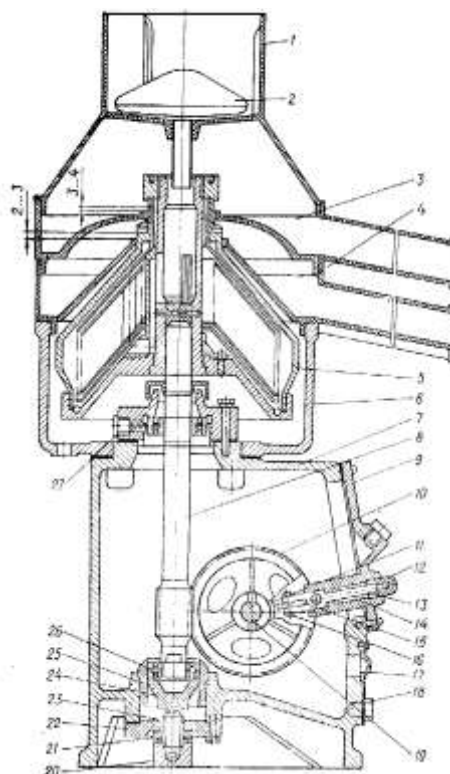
Сепаратор сливковідокремлювач ОСБ: 1 – поплавок камера; 2 – поплавок; 3 – прийомник для сливок; 4 – прийомник для обезжиреного молока; 5 – барабан; 6 – чаша станини; 7 – станина; 8 – вертикальний вал; 9 – кришка; 10 – черв’ячна шестерня пульсатора; 11 – шестерня пульсатора; 12 – ковпачок пульсатора; 13 – шток пульсатора; 14 – пружина пульсатора; 15 – ексцентрична шестерня пульсатора; 16 – вісь ексцентричної шестерні; 17 – покажчик рівня масла; 18 – пробка; 19 – горизонтальний вал; 20 – контргайка; 21 – контргайка; 22 – кришка нижньої опори вертикального вала; 23 – гвинт підп’ятника; 24 – п’ята; 25 – стакан; 26 – радіально-упорний підшипник; 27 – пружна опора.
